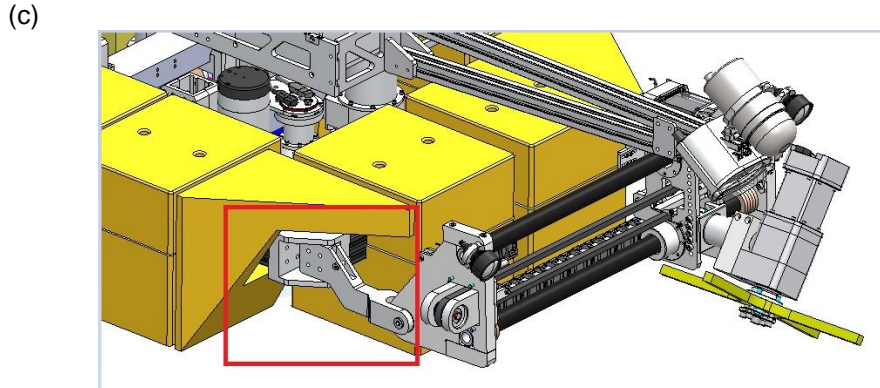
Detalhes do conjunto mecânico proposto para fixação do módulo de limpeza no chassi do robô MCCR.
